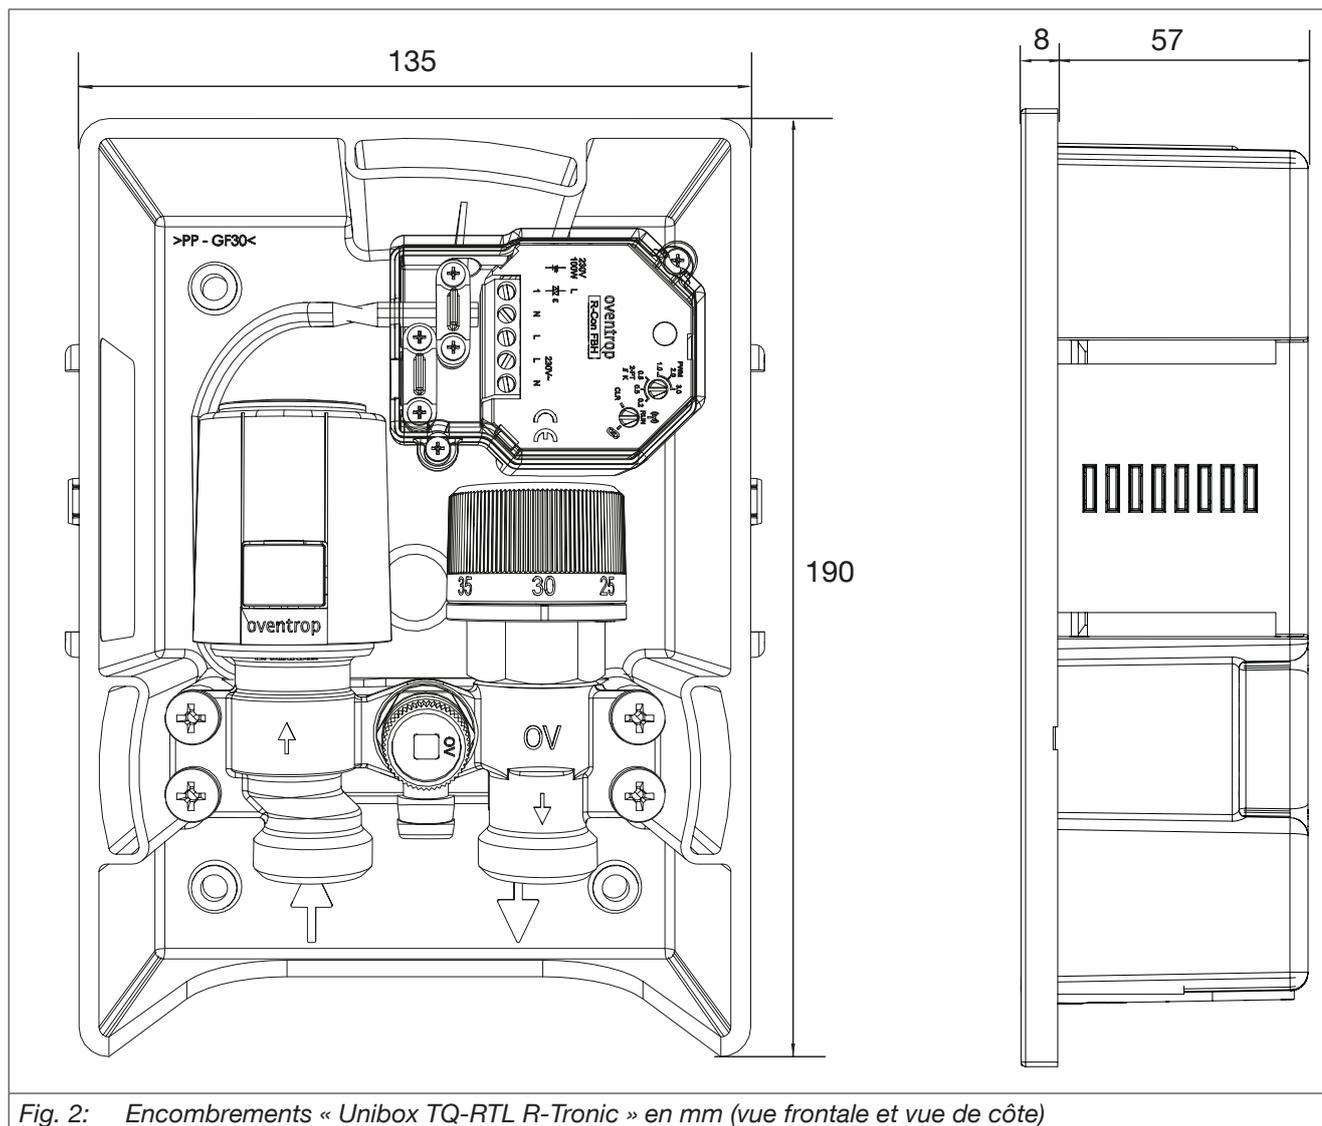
Encombremments « Unibox TQ-RTL R-Tronic » en mm (vue frontale et vue de côté)
